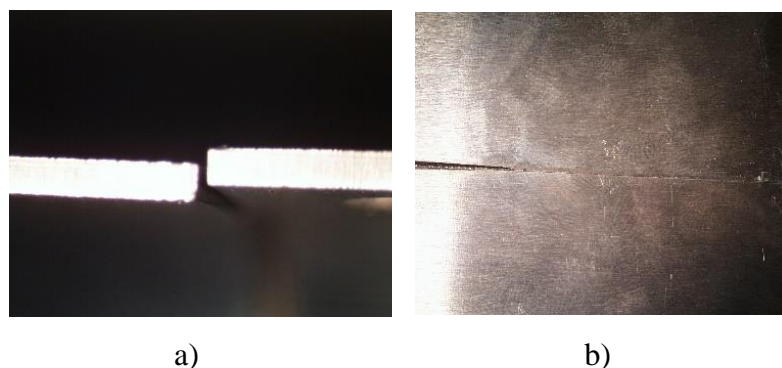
a) Desalinhamento dos provetes após a soldadura; b) Falta de penetração.
